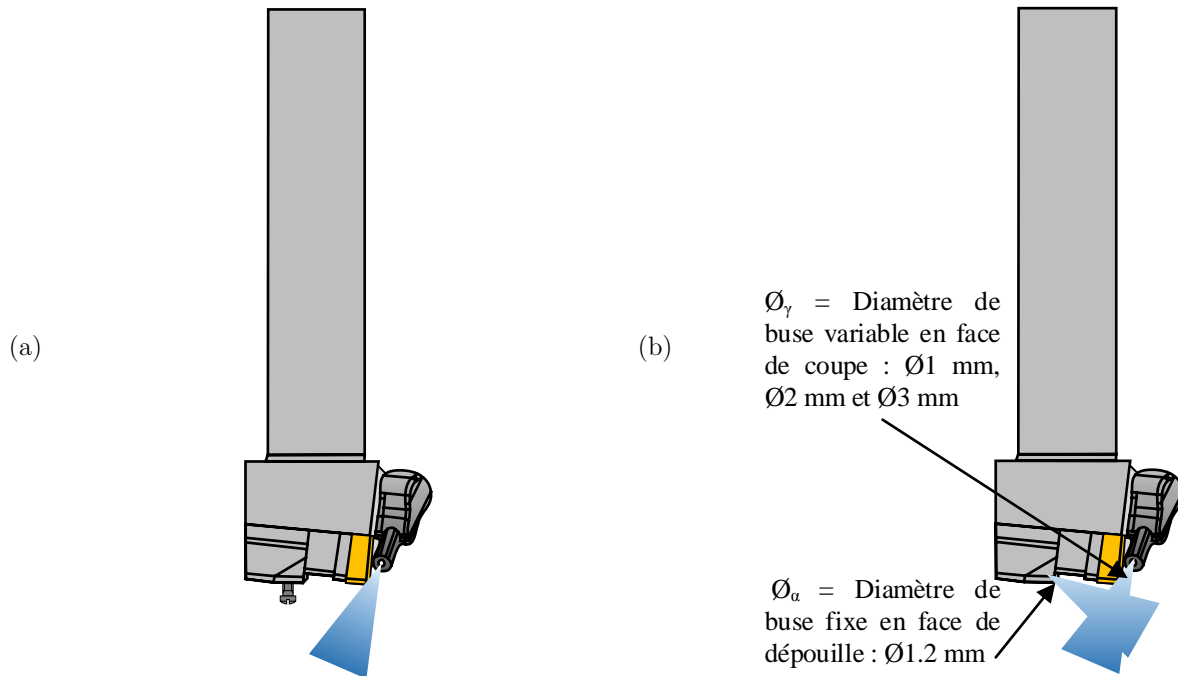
Stratégie de pulvérisation du LN₂ pour le tournage en chariotage du Ti6Al4V ; outil PCLNL - 12 modifié pour assistance cryogénique ; a) Projection face de coupe ; b) Projection face de coupe + dépouille
